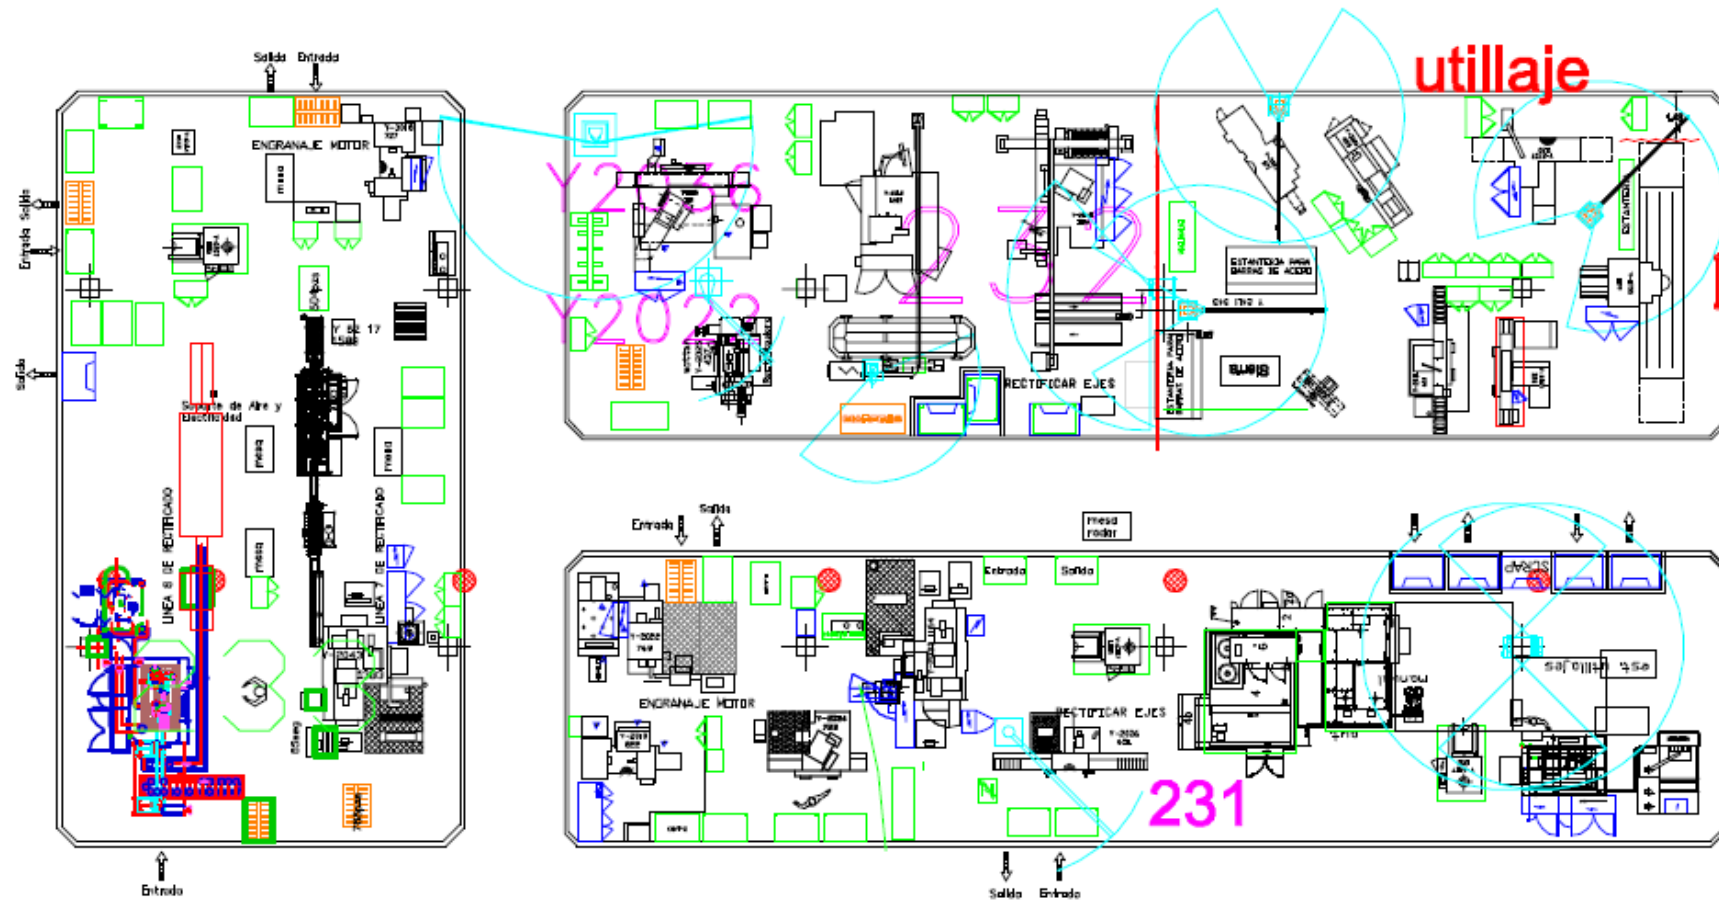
Utillaje, células de rectificado de ejes y engranajes de transmisión y líneas 7 y 8 de rectificado de engranajes motor.
